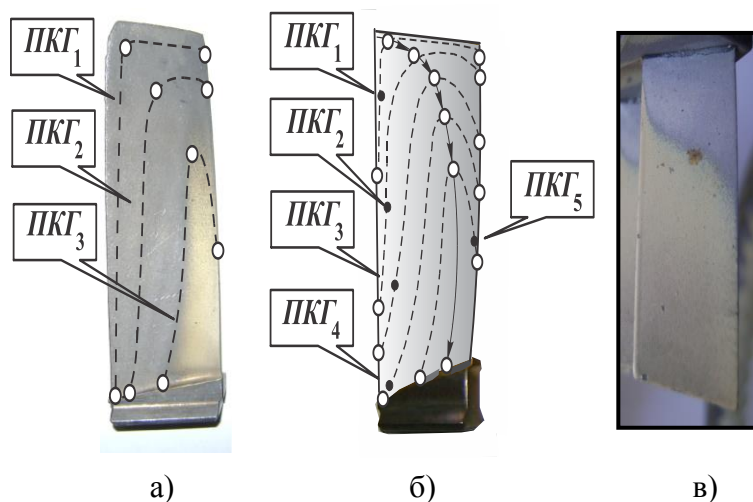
Лопатки компрессора со схемами ПКГ износа покрытия: а – общий вид рабочей лопатки с тремя ПКГ (5-я группа лопаток); б – схема рабочей лопатки с пятью ПКГ (5-я группа лопаток); в – общий вид лопатки НА статора с ПКГ (3-я группа лопаток)
